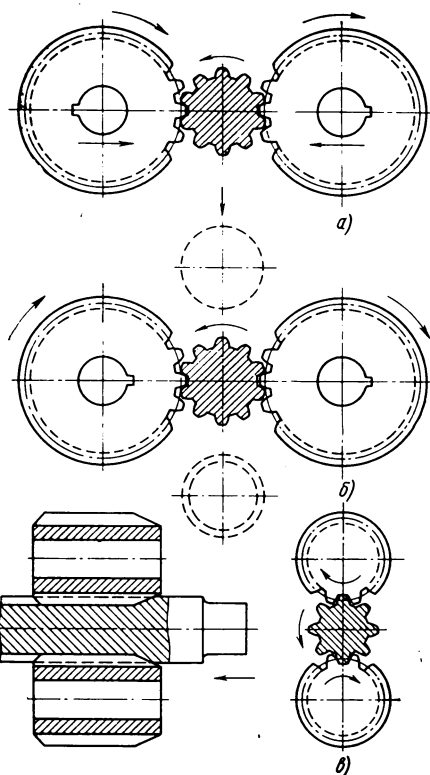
Схема накатывания зубьев вала круглыми зубчатыми роликами:
